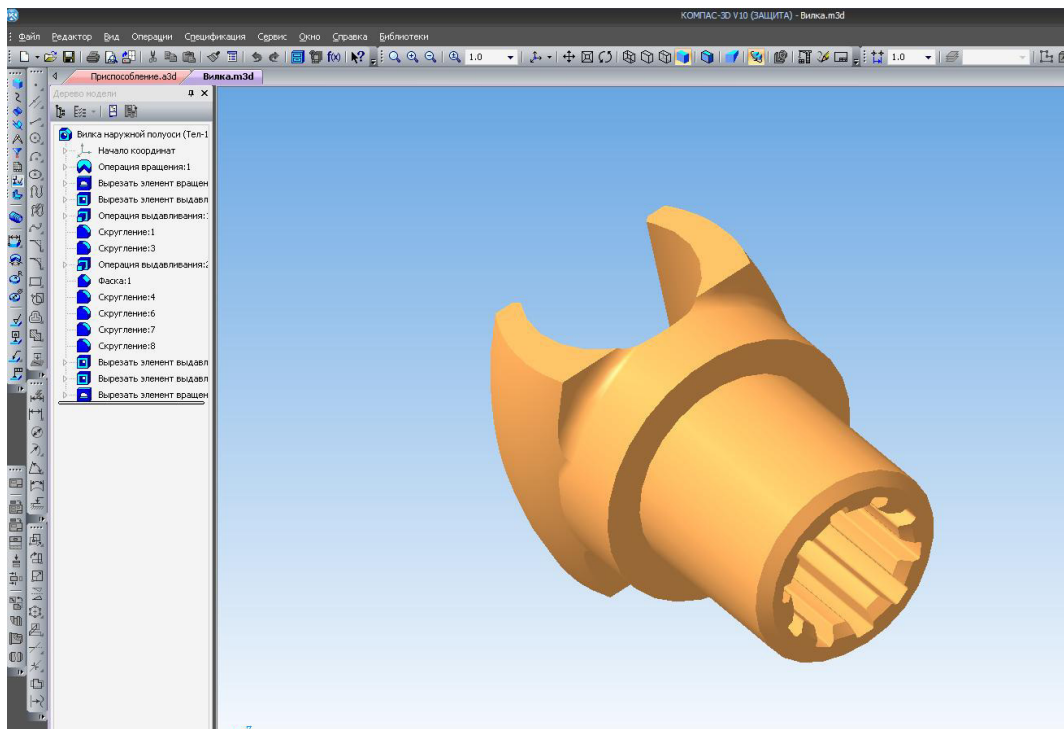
3D модель вилки наружной полуоси 5557X-2303072
